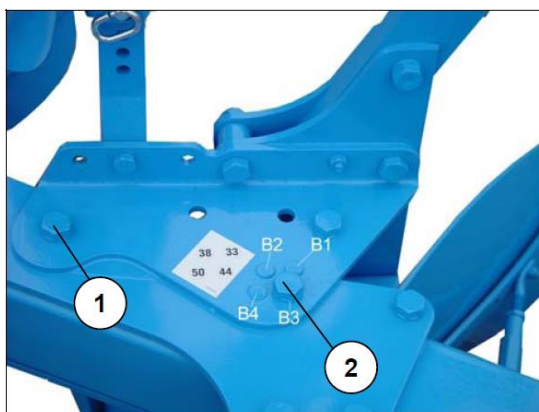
Встановлення робочої ширини захвату корпусу
